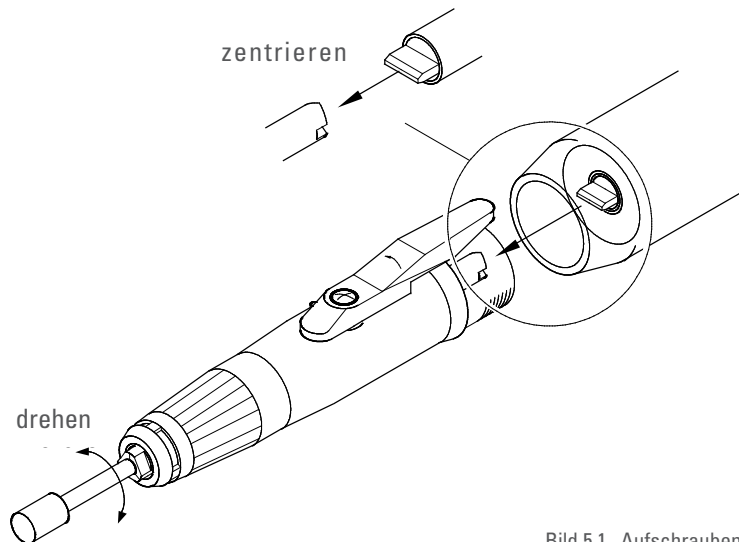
Aufschrauben des Handstückes (Symbolzeichnung)
